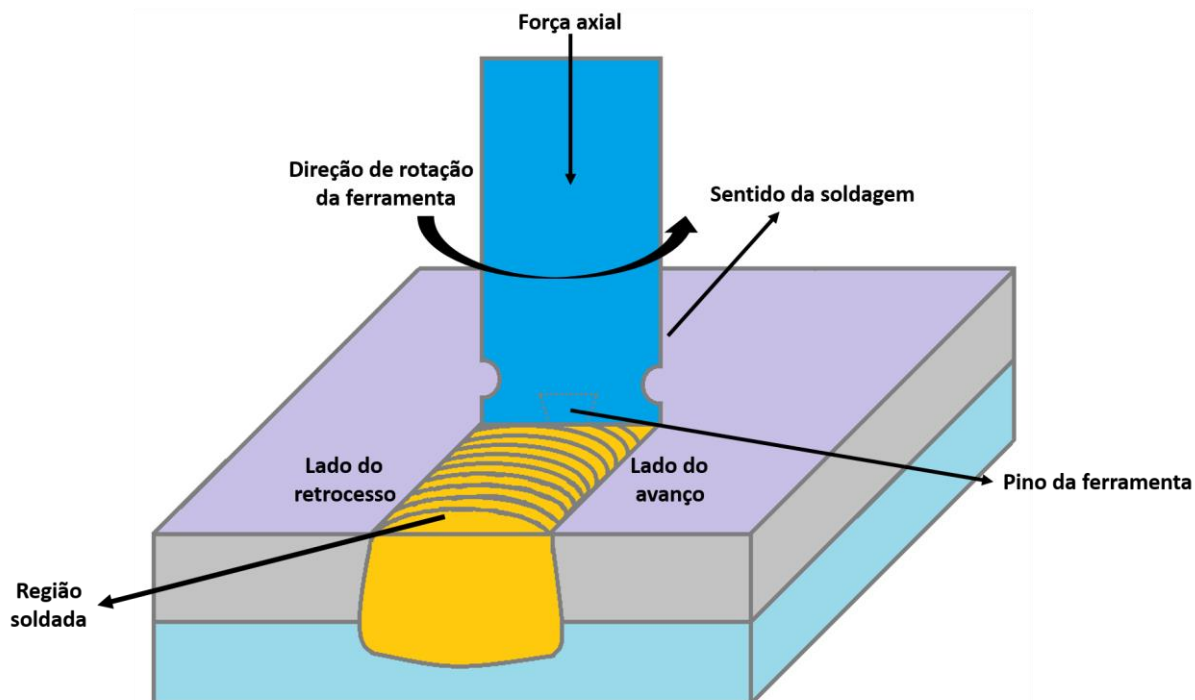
Representação esquemática dos movimentos da ferramenta de soldagem do processo por fricção linear (Fonte: próprio autor).
